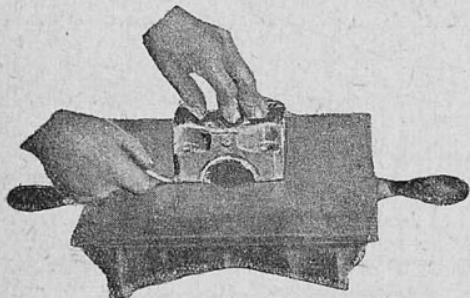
Проверка плоскости соединения половинок подшипника по проверочной плите
